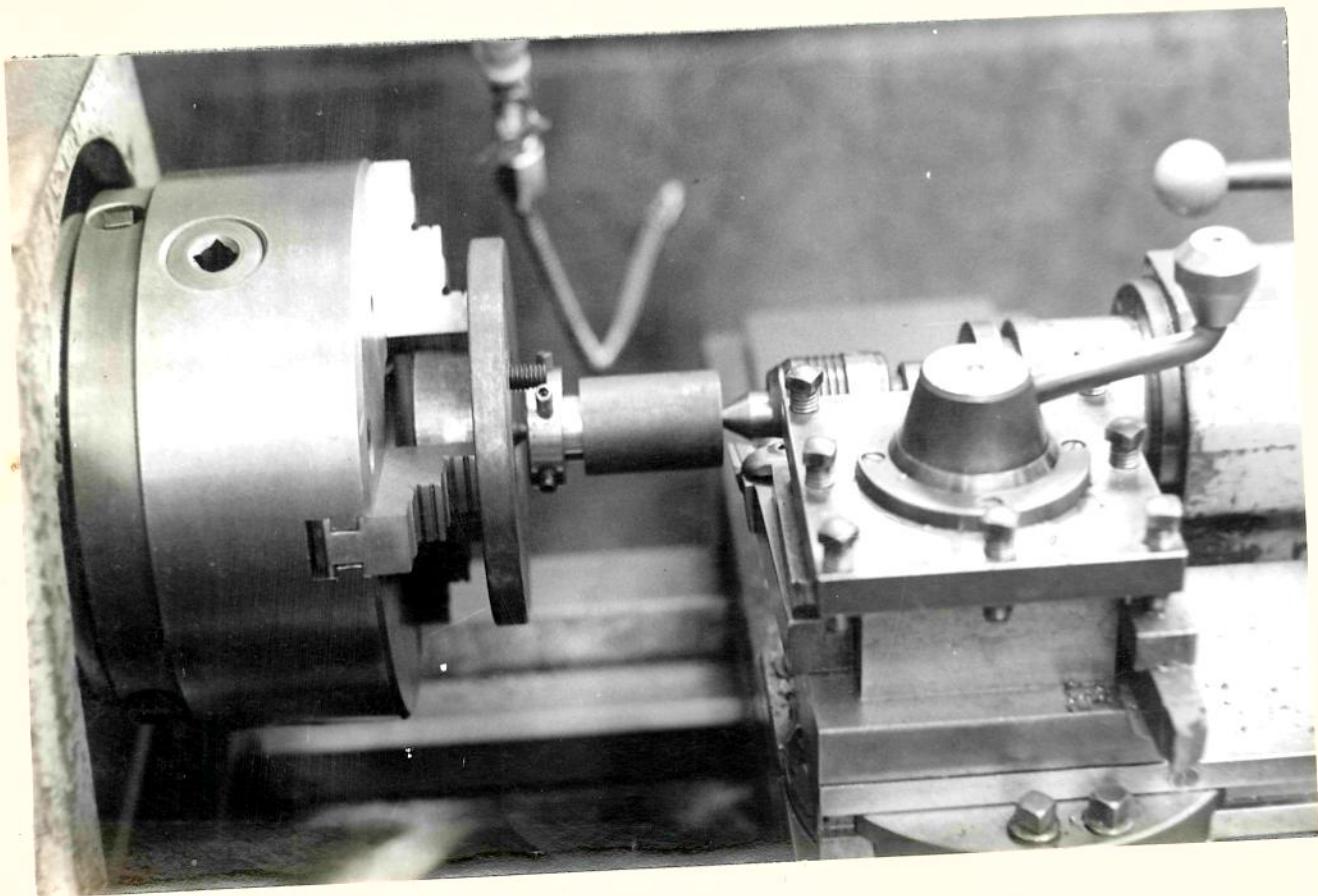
Posicionamento da ferramenta para início de usinagem
